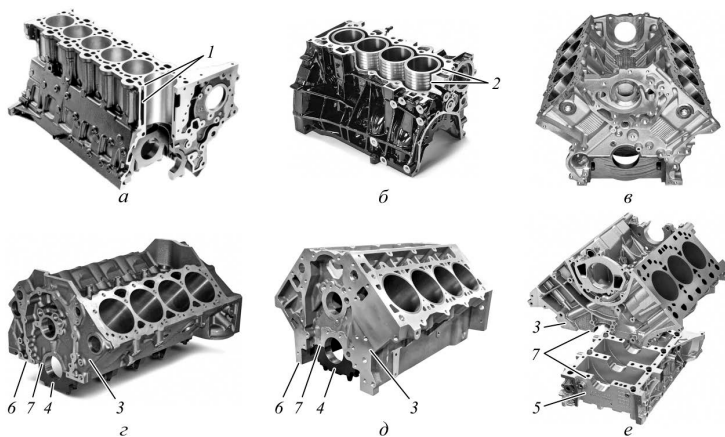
Конструкции блоков цилиндров: *а* – рядное расположение цилиндров с закрытым исполнением рубашки охлаждения; *б* – рядное расположение цилиндров с открытым исполнением рубашки охлаждения; *в* – V-образное рядное расположение цилиндров; *г* – блок-картер с плоскостью разъема по оси коленчатого вала; *д* – блок-картер с плоскостью разъема ниже оси коленчатого вала; *е* – блок-картер с опорной плитой; 1 – закрытое исполнение рубашки охлаждения; 2 – открытое исполнение рубашки охлаждения; 3 – блок-картер; 4 – крышка коренного подшипника; 5 – опорная плита; 6 – плоскость разъема блок-картера; 7 – плоскость разъема коренного подшипника
